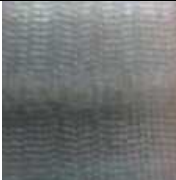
Образование шероховатости при фрезеровании выпуклых поверхностей для стратегий «3» и «4»
